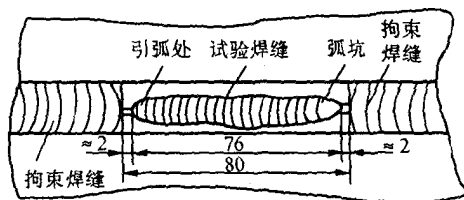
采用自动送进装置焊接的试验焊缝
